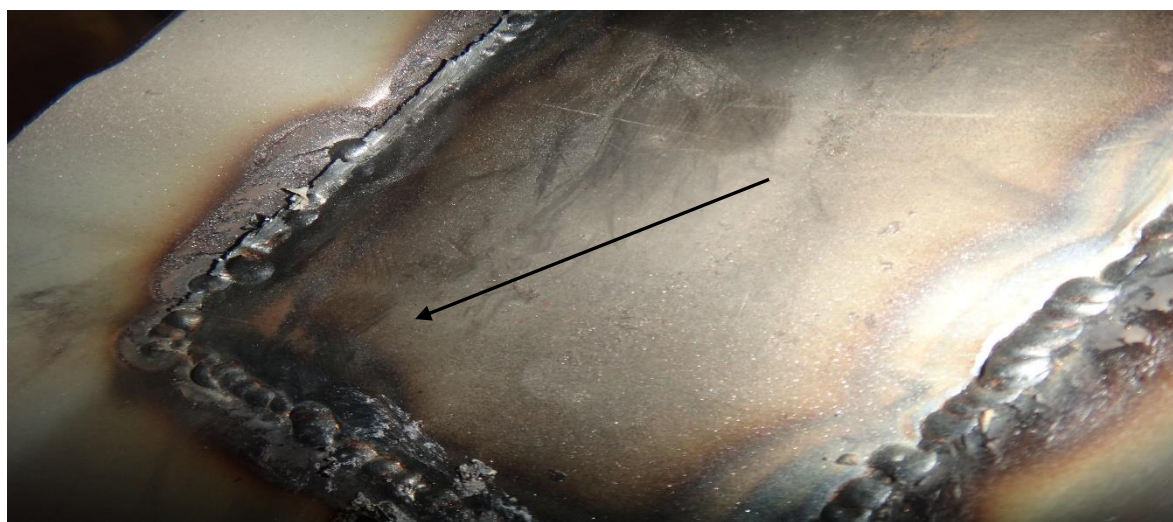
Сварные швы с обратной стороны маркируемой панели
